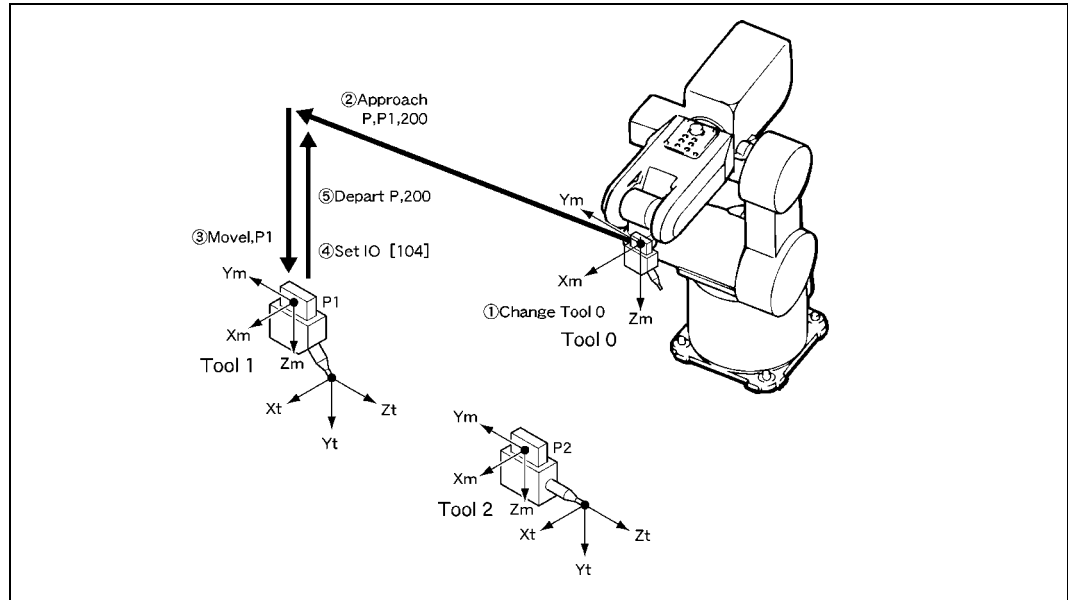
Verfahrenweg zur Freigabe von Endwerkzeug 1
